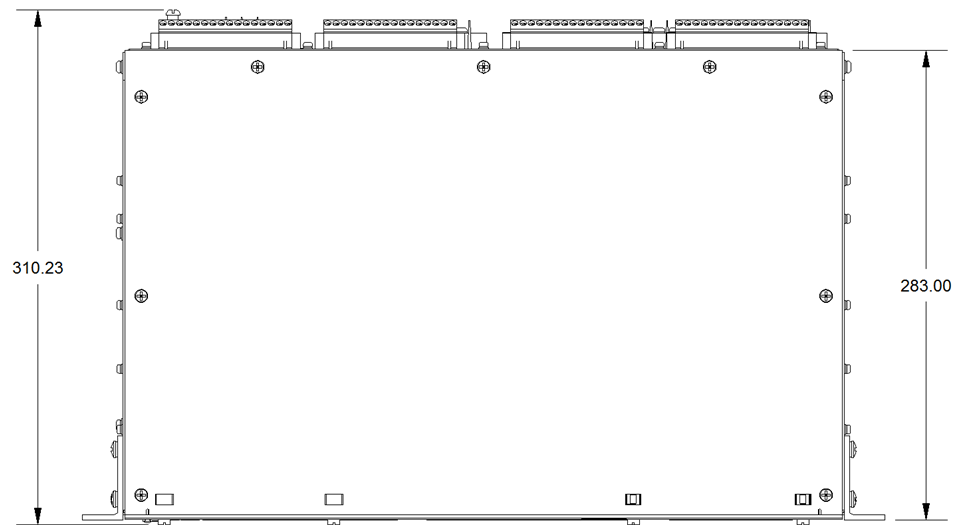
Dimensions physiques - Vue du dessus – Famille ALP-4000
